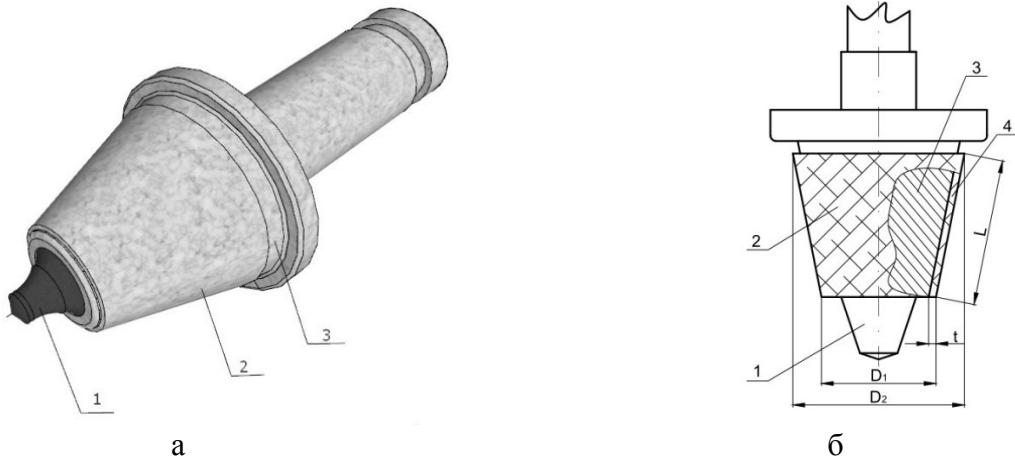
Общий вид зуба (а) и схема нанесения покрытия (б): 1 – наконечник твердосплавной; 2 – рабочая поверхность корпуса; 3 – корпус зуба; 4 – защитное покрытие
